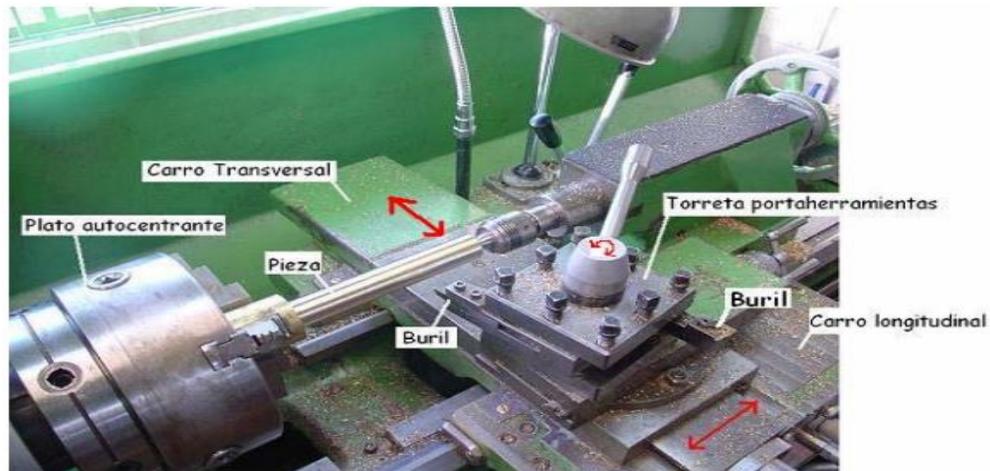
Partes Principales Torno, Torreta Portaherramientas.
